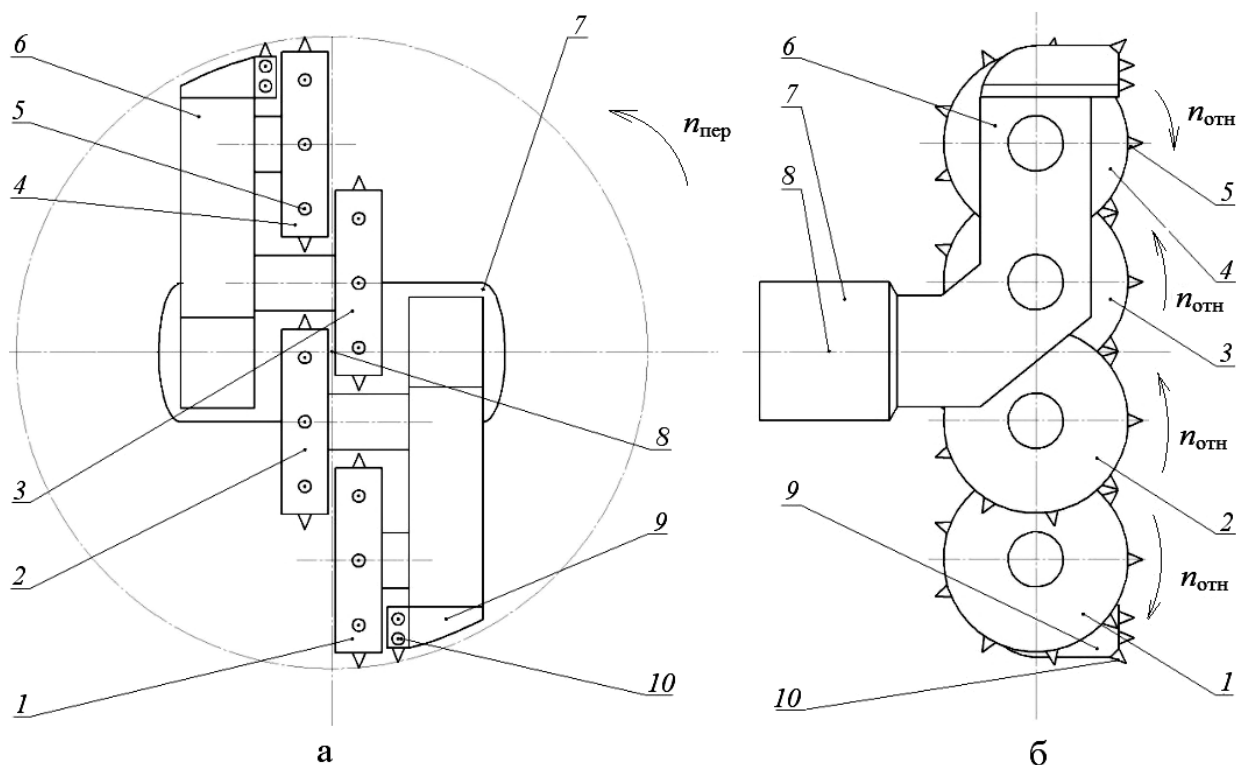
Четырехдисковый пространственный планетарный исполнительный орган, реализующий перекрестную схему резания: а – вид спереди; б – вид сбоку
